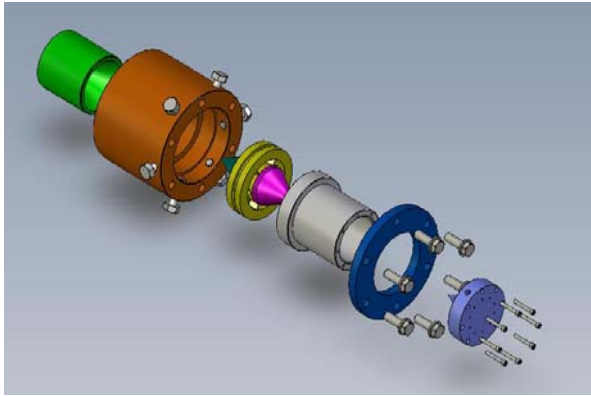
Vista en explosionada del modelo del cabezal diseñado y construido por los autores para la extrusora de la FIMCP
